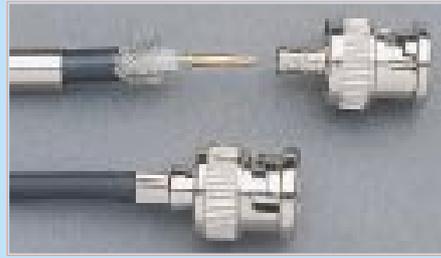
Montierter und teilmontierter BNC-Stecker in Crimptechnik.
